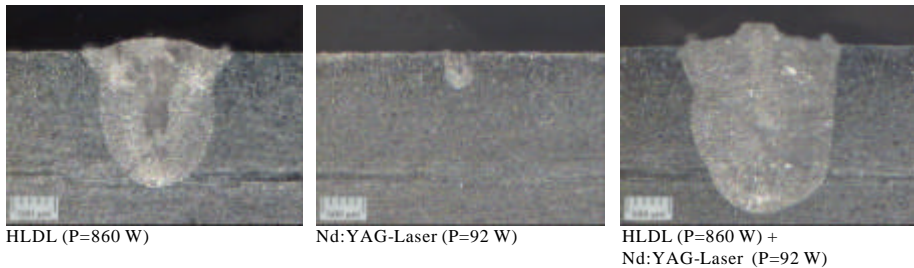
Nahtquerschnitte von Blindschweißungen in Edelstahl 1.4301 (Dicke 3,0 mm), $v=5$ mm/s
